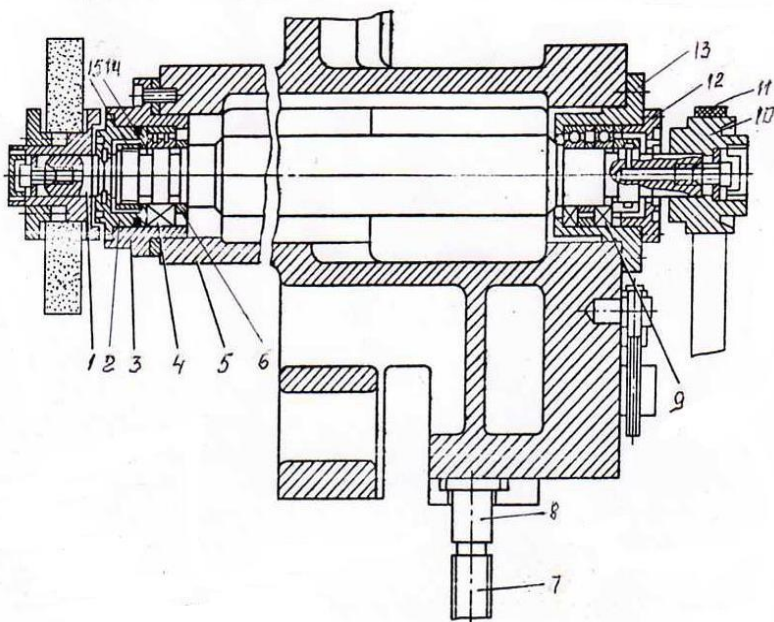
Шлифовальная головка станка мод. 3Е711В
